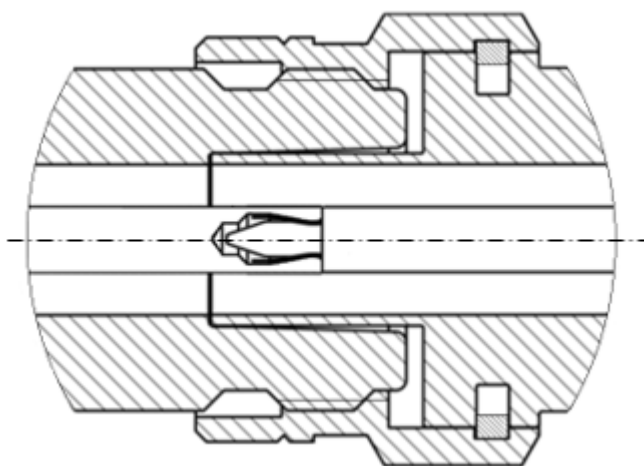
Соединители тип N (розетка слева, вилка справа)
